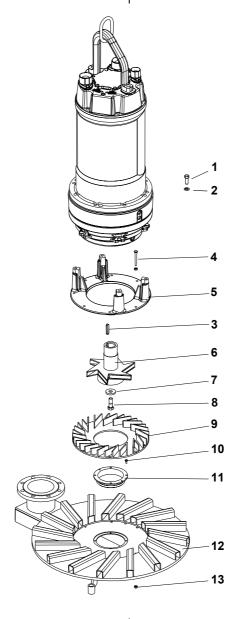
TA 901 - 2400 Hydraulik - zerlegt
